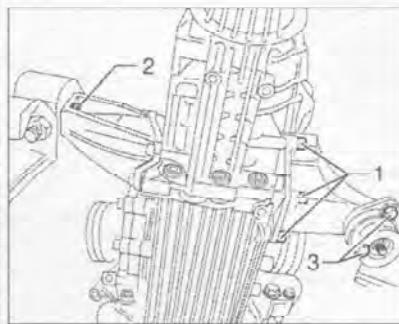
Отверните болты (1 и 3) и снимите правую опору коробки передач. Отверните болт (2) и отсоедините правую опору коробки передач.
